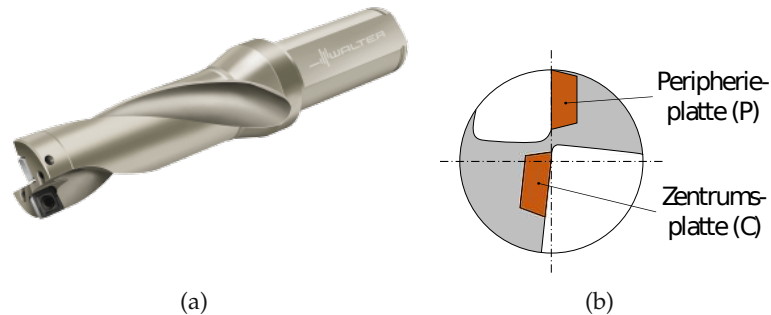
(a) Wendeplattenbohrer mit gedrehten Spannuten der Walter AG [36] sowie (b) Skizze der Bohrspitze
